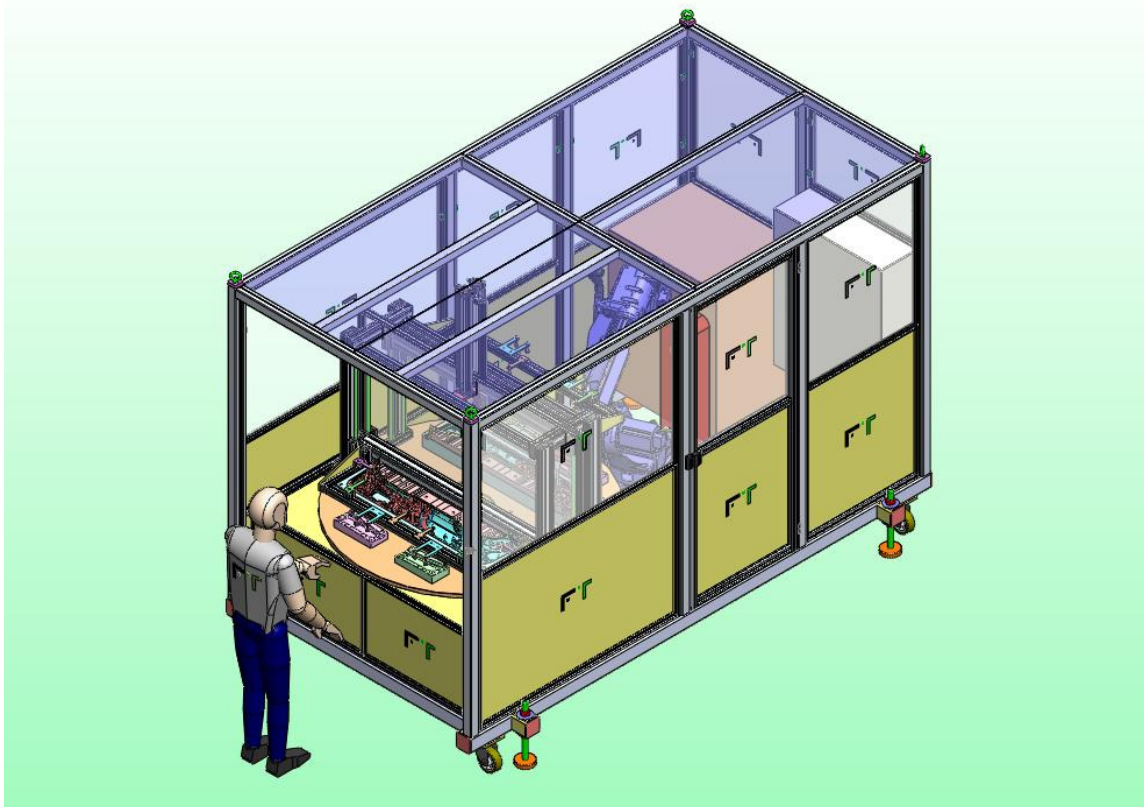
Célula de soldadura por ultra-sons com robô de 6 eixos
